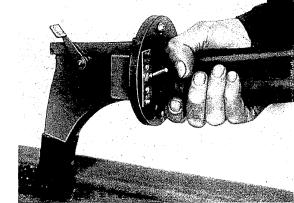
Полуавтоматическая сварочная головка ГСП-2.
